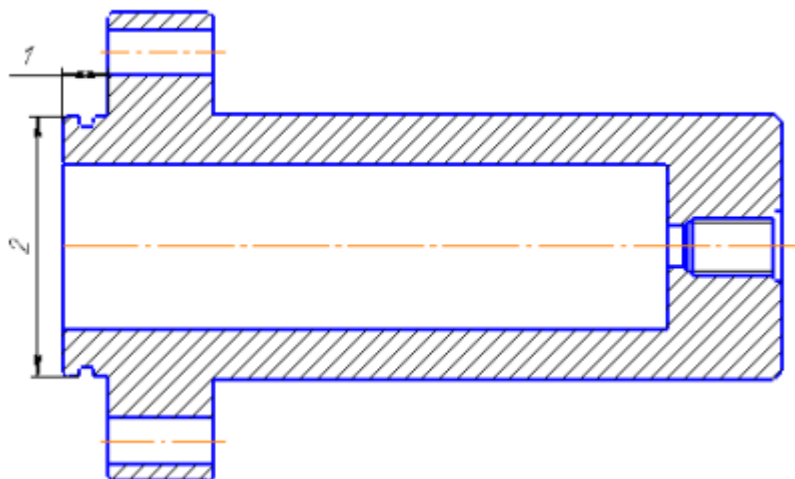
Креслення оброблюваної деталі з необхідними розмірами
